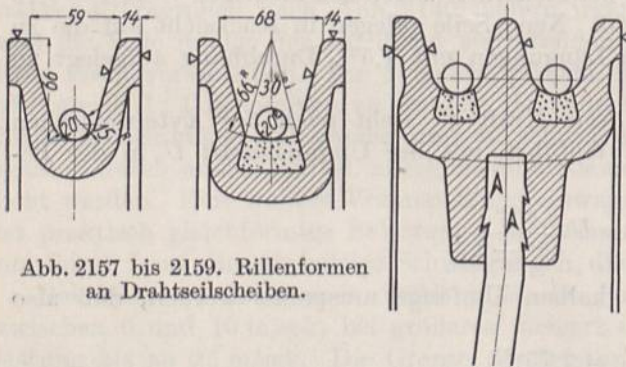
bis 2159. Rillenformen an Drahtseilscheiben.
